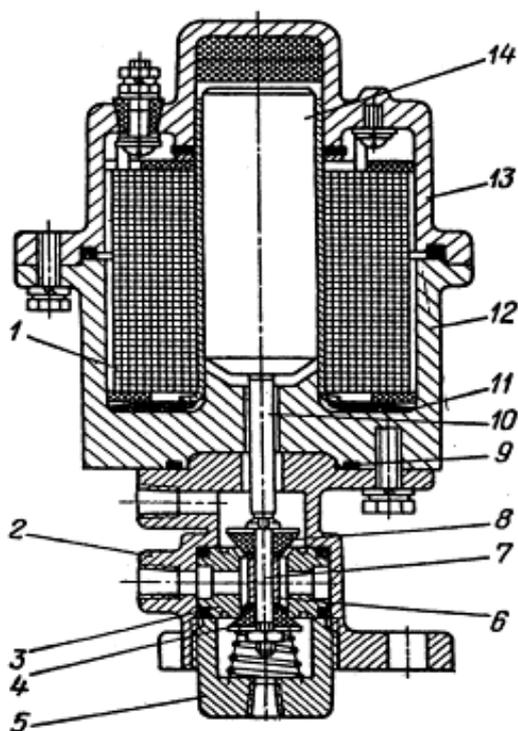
Электромагнитный пневматический клапан: 1 – электромагнит; 2 – корпус клапана; 3 – седло клапана; 4 – впускной клапан; 5 – пробка клапана; 6 – распорная втулка; 7 – стержень клапана; 8 – выпускной клапан; 9 – уплотнительное кольцо; 10 – шток; 11 – дисковая пружина; 12 – корпус; 13 – крышка; 14 – сердечник
